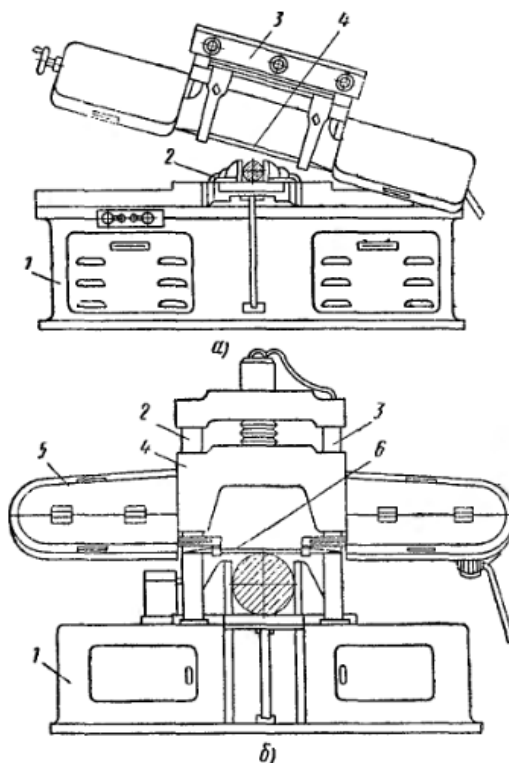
Ленточно-пильные станки: а - консольного типа; б — фронтального типа
